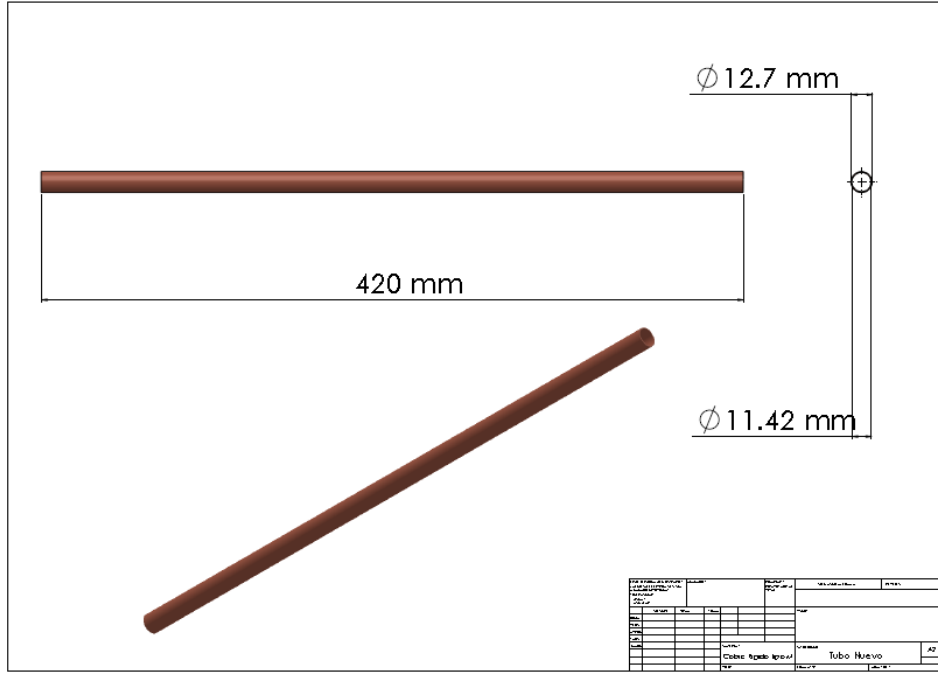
Plano de Tubo de cobre, Fuente Solidworks 2014
